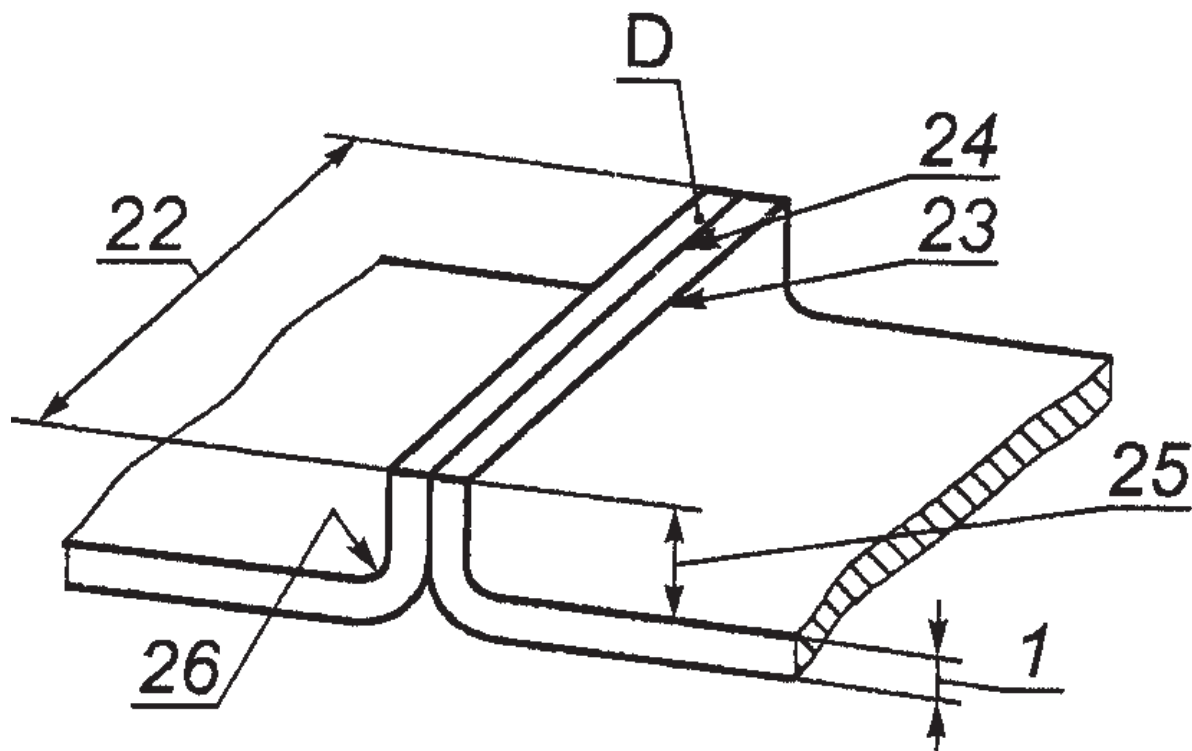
Подготовка под сварку стыкового соединения с отбортовкой кромок Figure 8. Preparation for butt weld between plates with raised edges Figure 8. Assemblage bords
